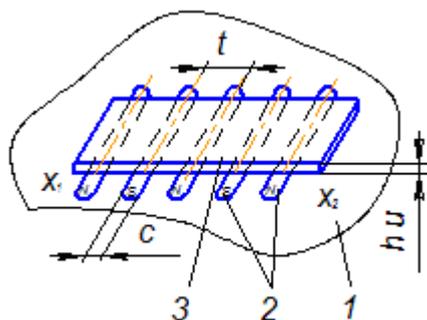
Сечение плоской детали, закрепленной на магнитном приспособлении: 1 – рабочая поверхность приспособления; 2 – его полюсы; 3 – обрабатываемая деталь
